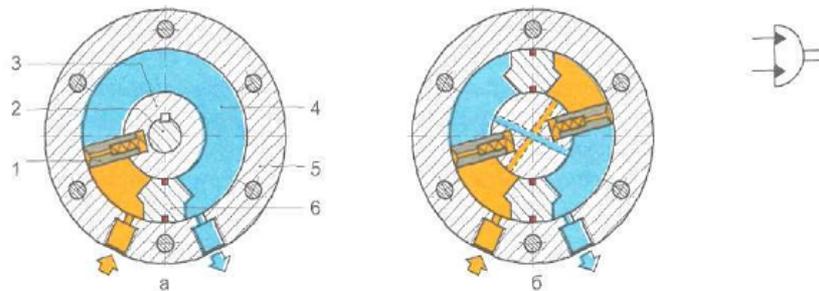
Пластинчатые поворотные гидродвигатели
